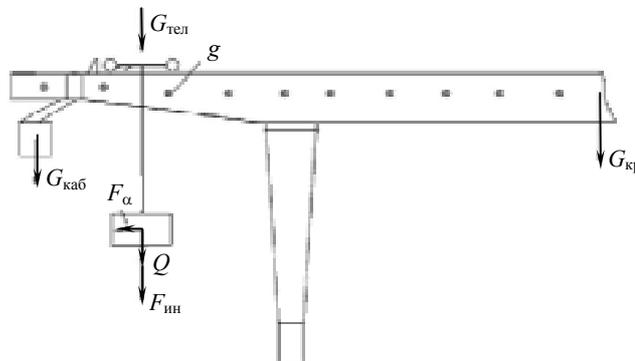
Расчетная схема нагрузок на металлоконструкцию крана
